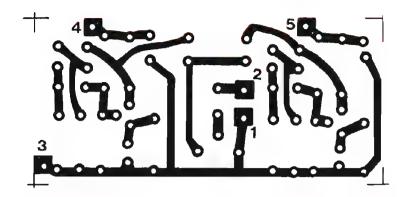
Disegno in grandezza reare del circuito stampato sul quale deve essere composto il dispositivo generatore di segnali audio.
